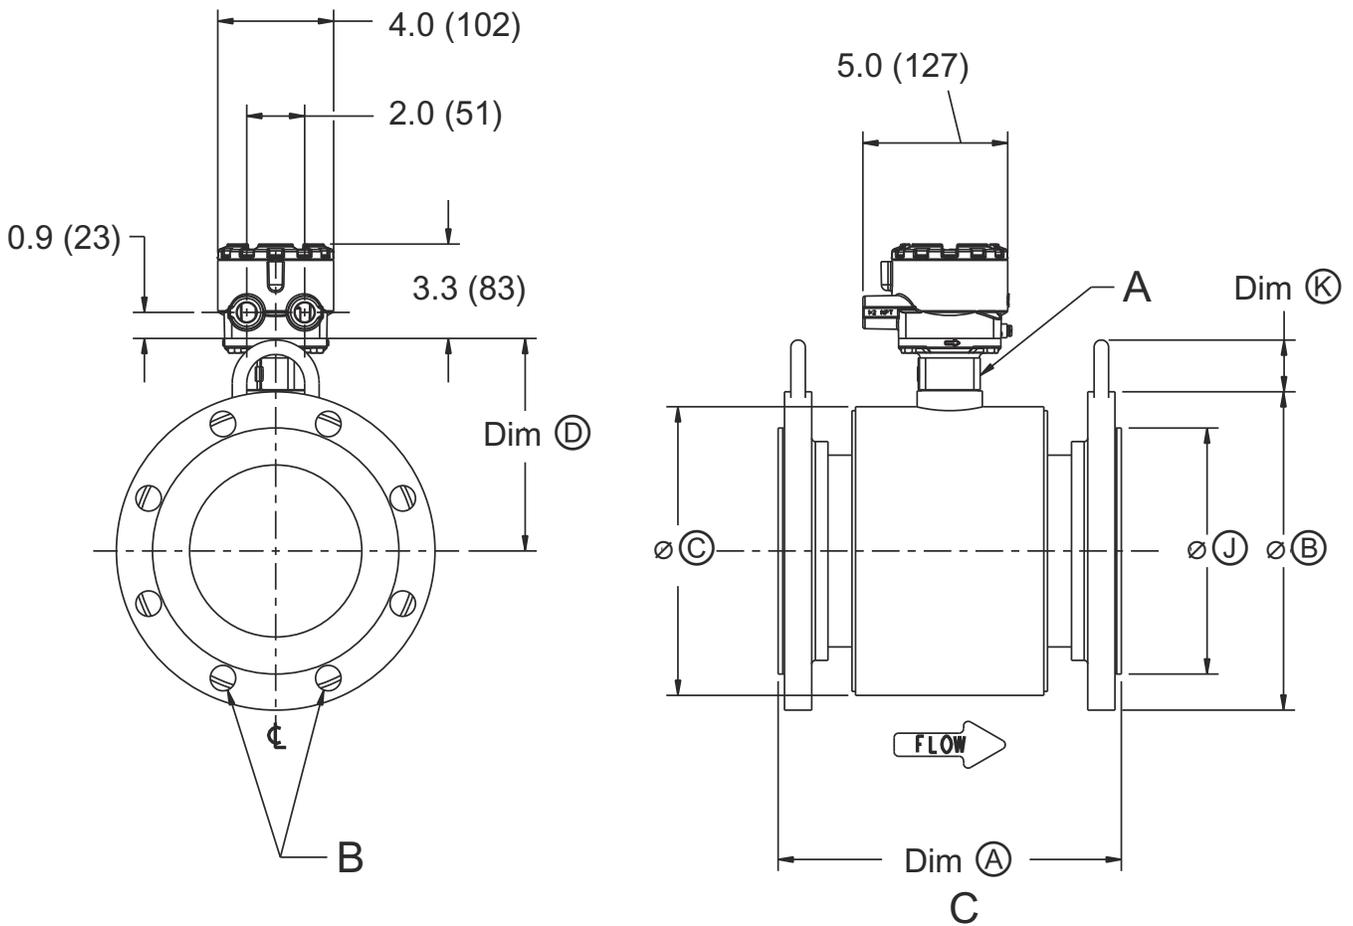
Детальный чертеж конфигурации корпуса катушки M1
